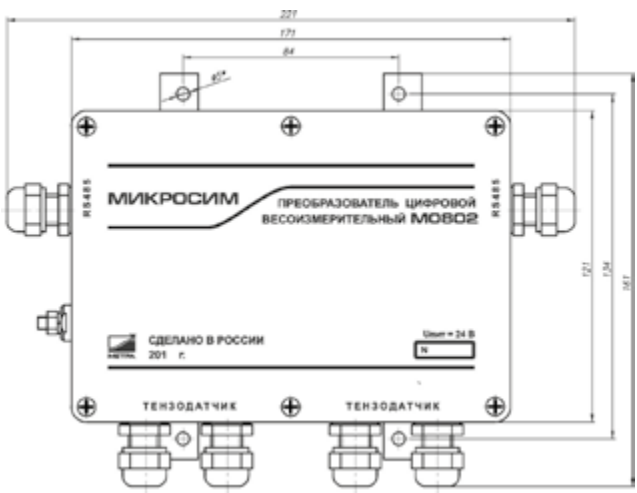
Внешний вид, габаритные и присоединительные размеры преобразователя
